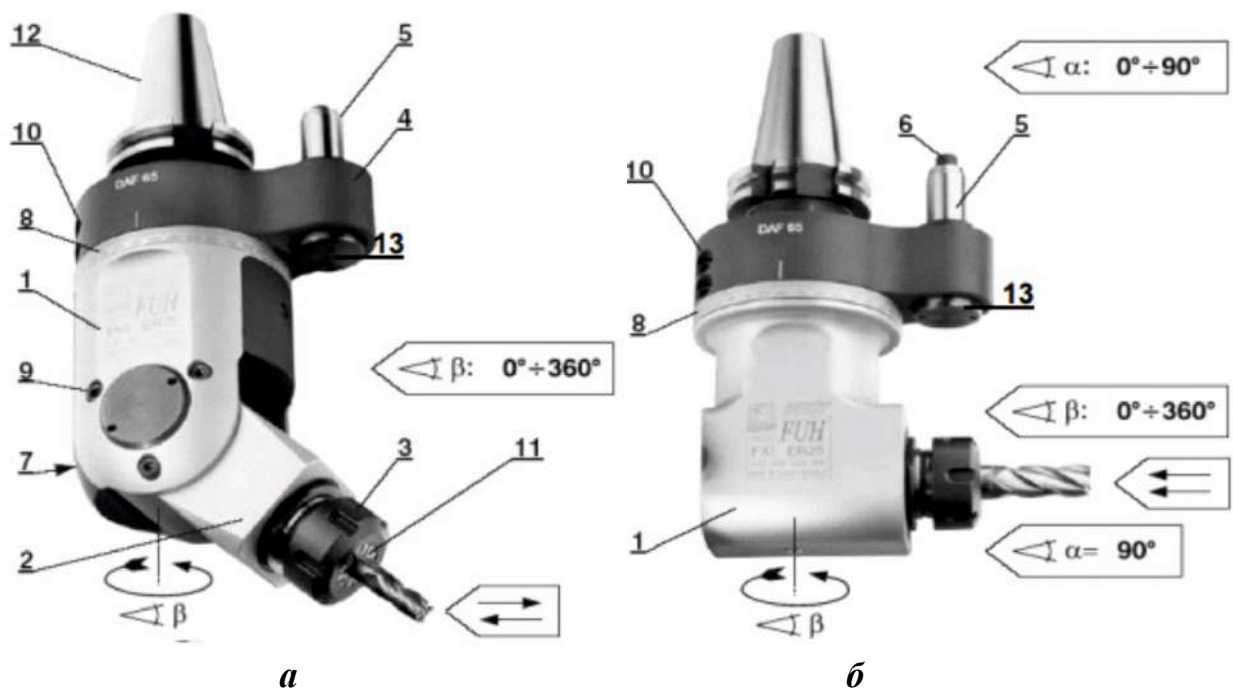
Конструкції кутових головок для фрезерного верстата:
